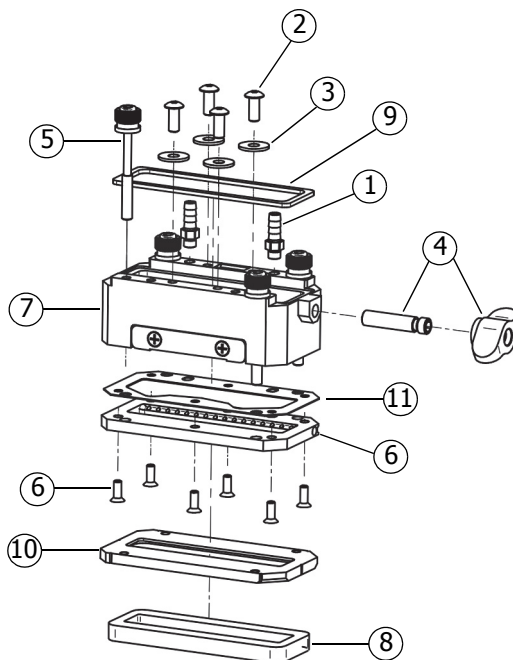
Сборочный чертеж держателя ПЭП HydroFORM
